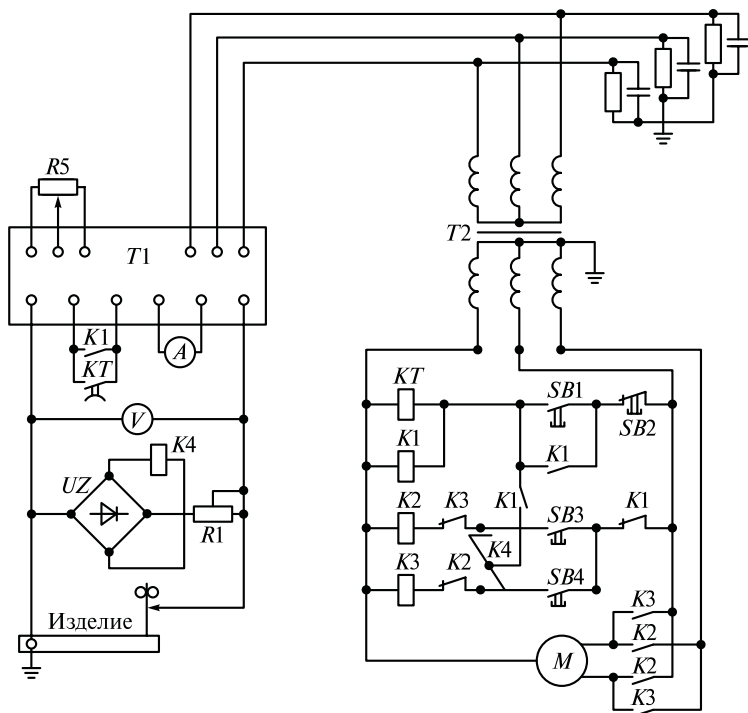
Электрическая схема сварочного трактора АДФ-1002:
